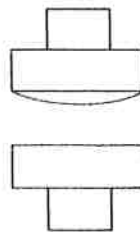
Desenho de contatos visando minimização da soldagem estática (Adaptado de Degussa) [7]
